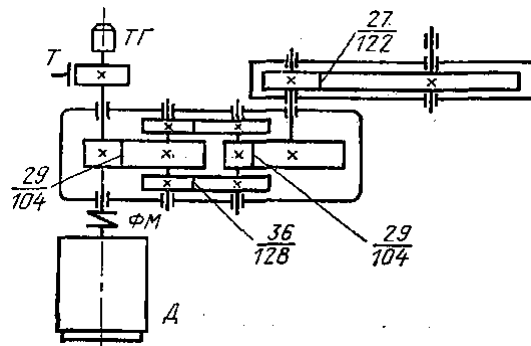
Схема механізму приводу роторного колеса екскаватора ЕРШР -1600
